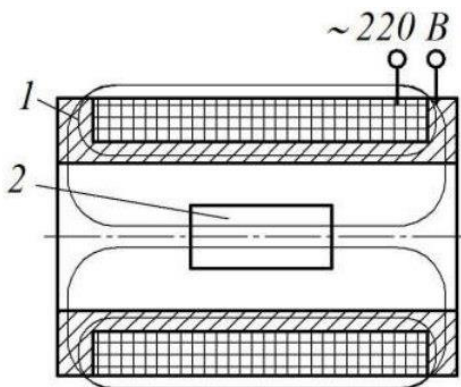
Обробка імпульсним магнітним полем: 1 – заготовка; 2 – соленоїд [27]
